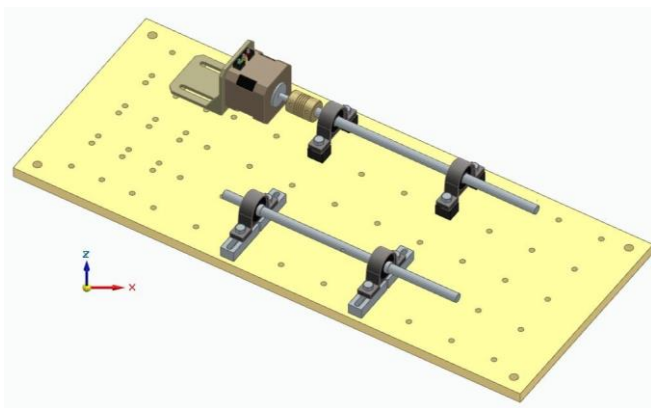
Projeto em 3D da planta didática. Fonte: Autores.
